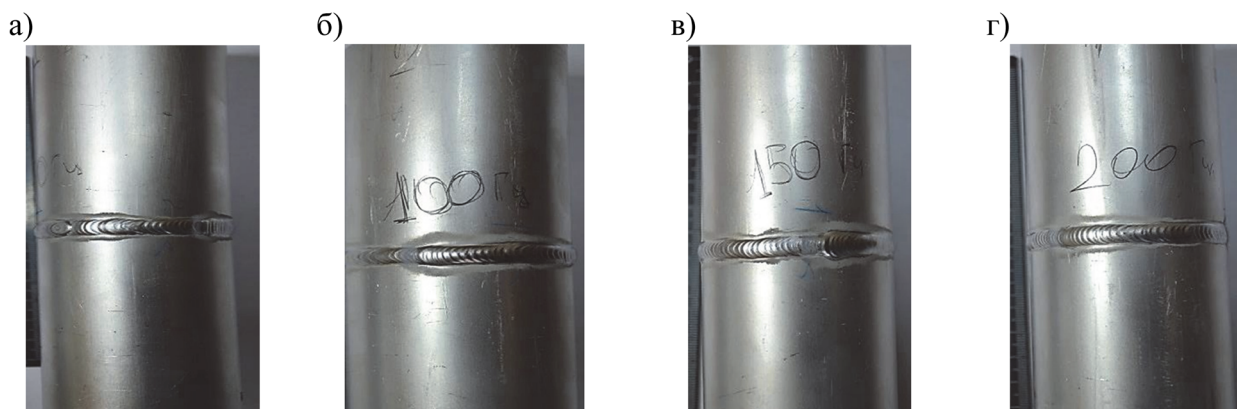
Полученные сварные образцы: а – образец 1; б – образец 2; в – образец 3; г – образец 4
